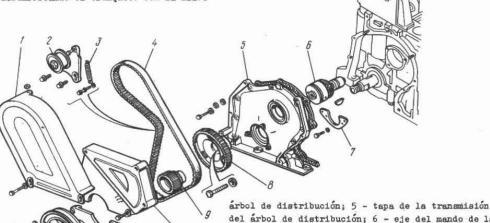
Despiece de la parte delantera del motor: 1 - tapa superior de protección; 2 - rodillo tensor; 3 - muelle tensor; 4 - correa de la transmisión del
